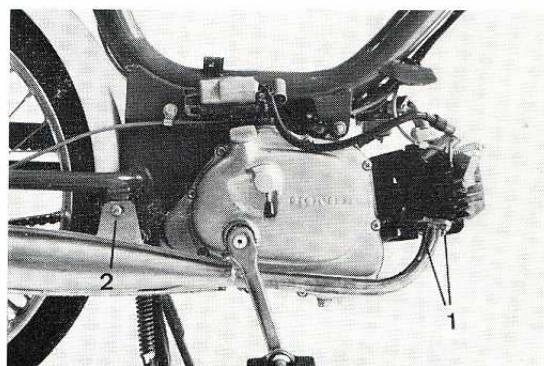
DEMONTAGE DU TUYAU D'ECHAPPEMENT.
